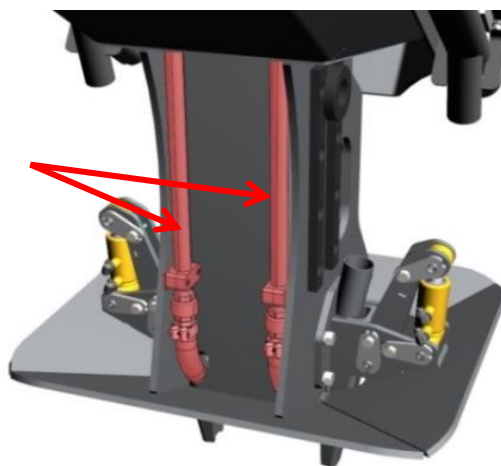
Sistema de irrigação pertencente ao cabeçote Bracke Planter P11.a. Fonte: Bracke Forest (2016)
